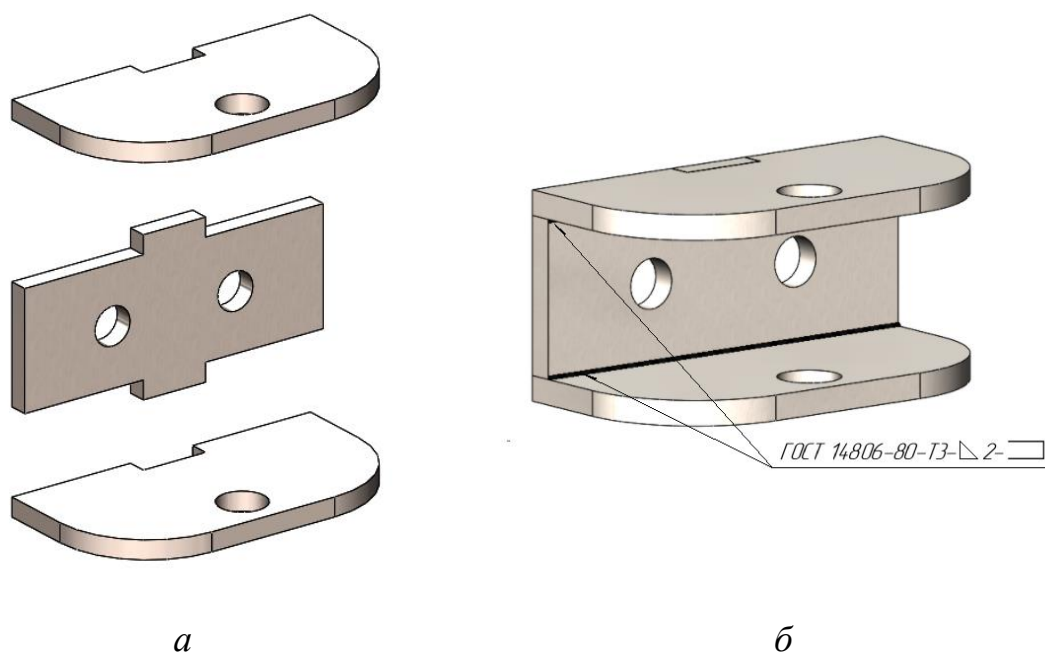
Сборка кронштейна крепления верхнего рычага: *a* – общий вид сборки; *б* – сварное соединение деталей.
